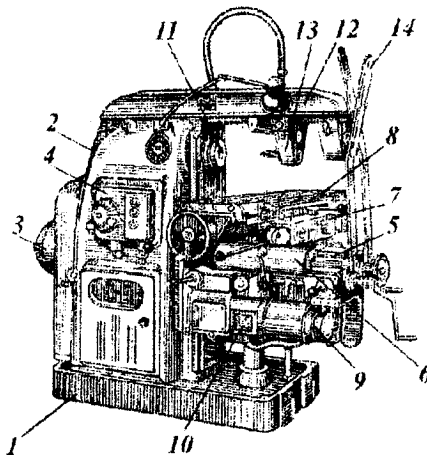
Горизонтально-фрезерний верстат 6М82
